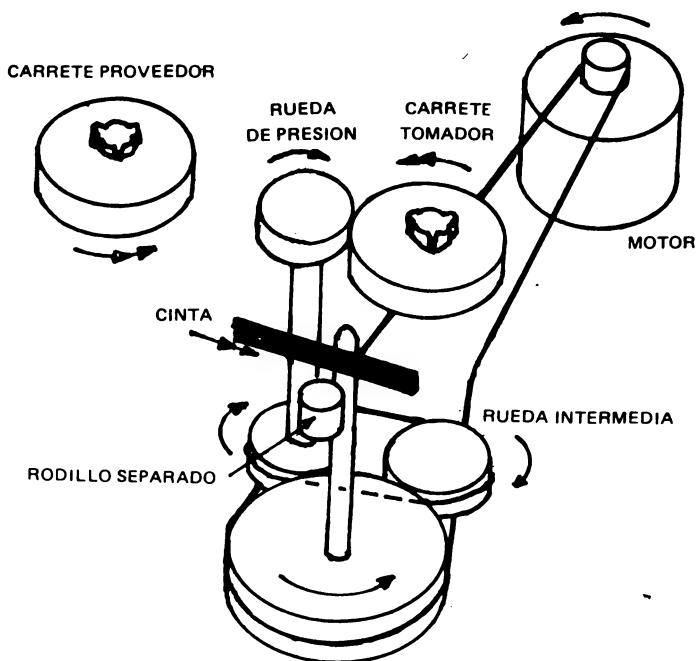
Disposición de la parte mecánica para el enrollado rápido. El carrete tomador es accionado por un juego de ruedas intermedias (del *Manual Técnico Grabadores PHILIPS*).
